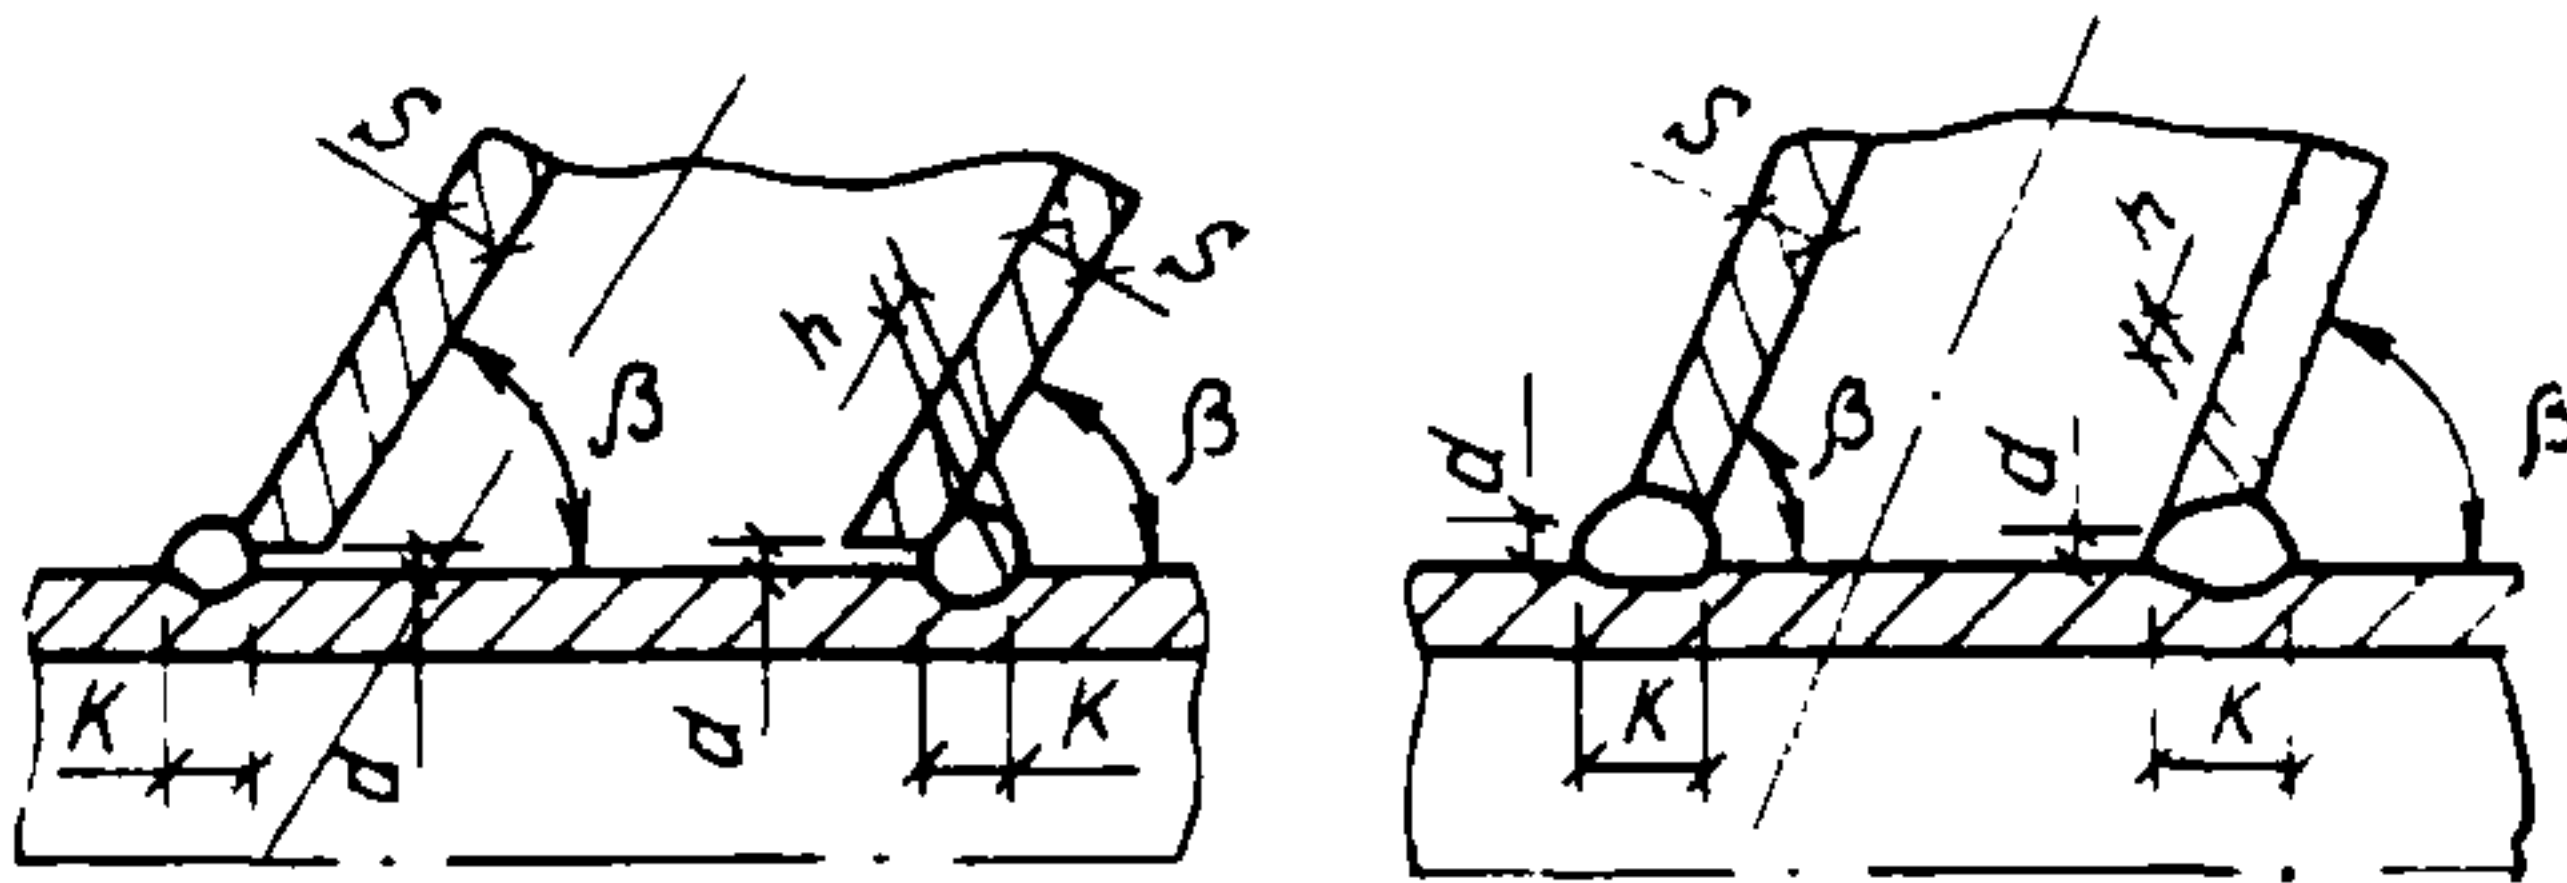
Виды и геометрические размеры швов сварных соединений
